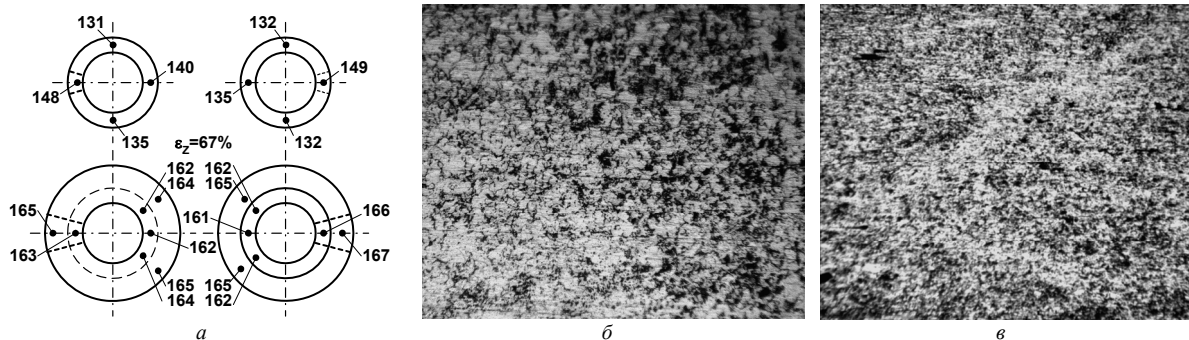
Результати замірів поверхневої твердості (шкала *HB*) кільцевої зварної заготовки (а) і фланцевої деталі (б) після штампування обкочуванням та межа між основним металом кільцевої заготовки та зоною зварного шва до деформування (а) та після штампування обкочуванням (г)
